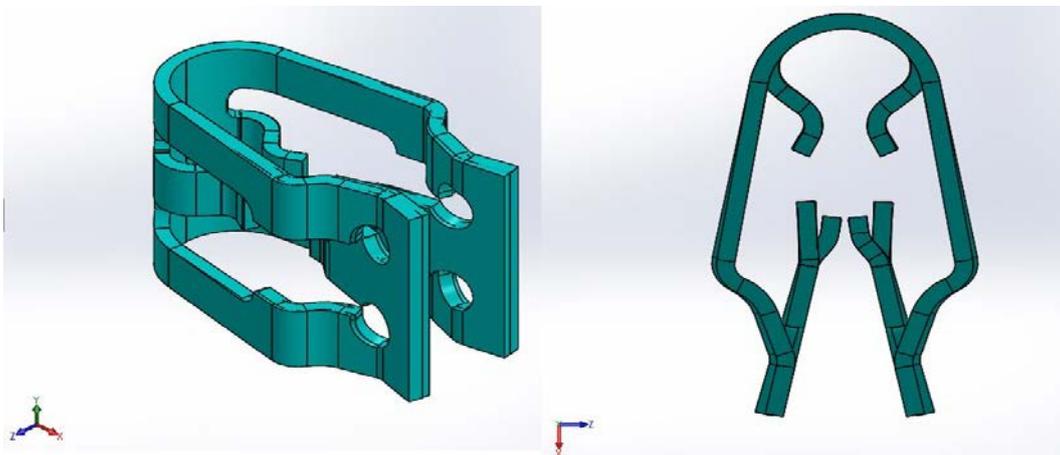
Grapa pieza END CAP y LOWER END PNL STRIP, W718896
